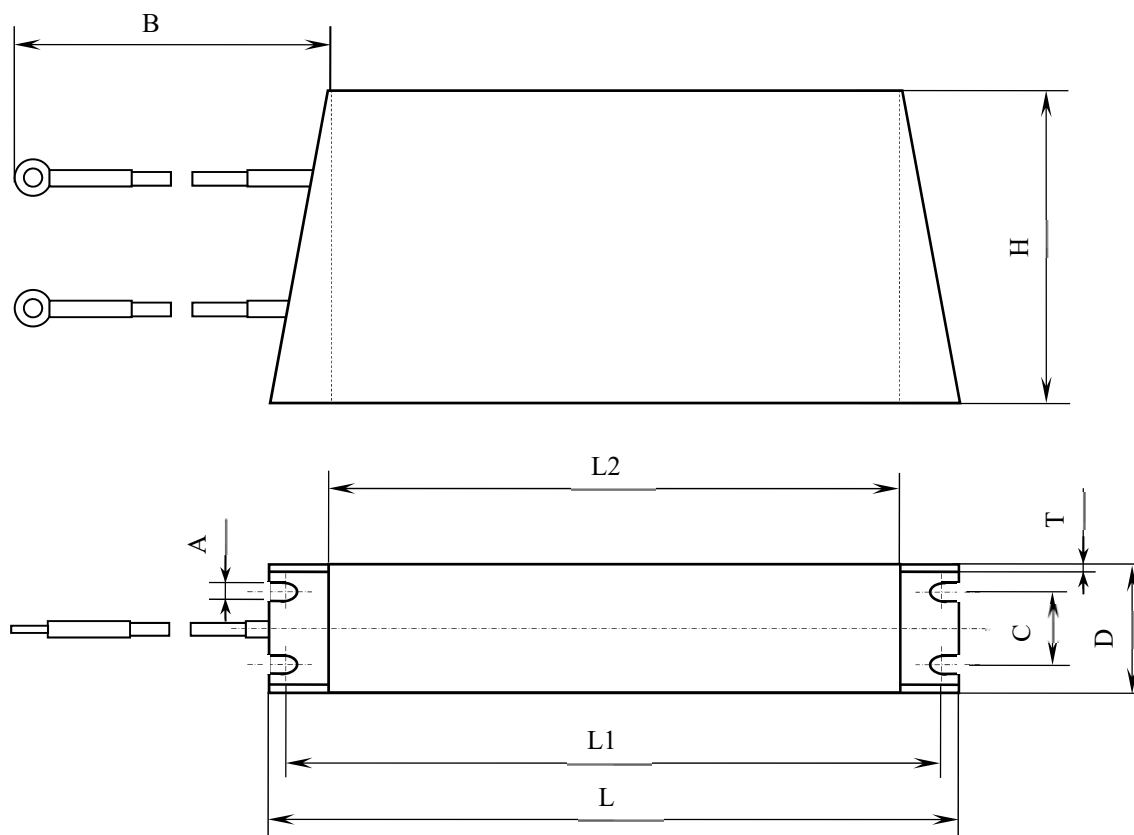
Габаритные и установочные размеры тормозного сопротивления RXLG
